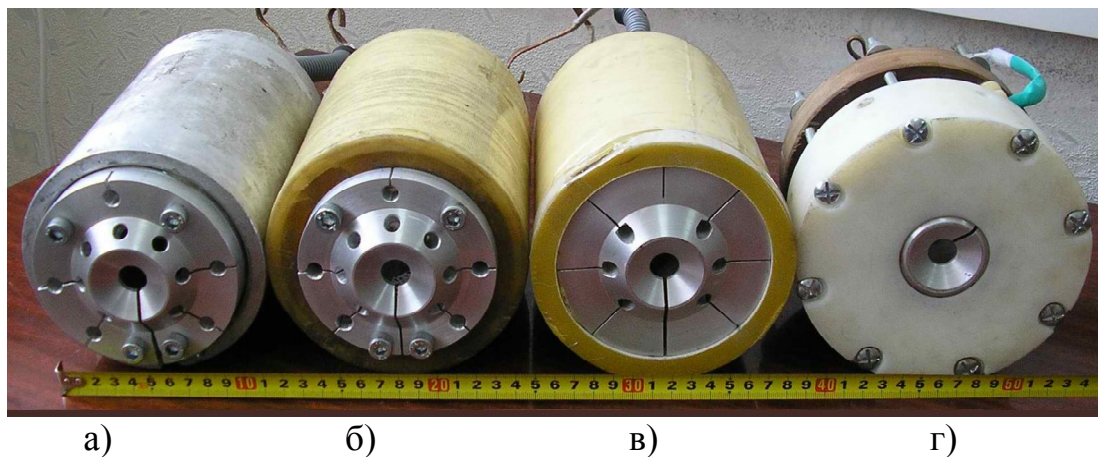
Внешний вид разработанных согласующих устройств: а) цилиндрическое с двумя вторичными разомкнутыми витками;
